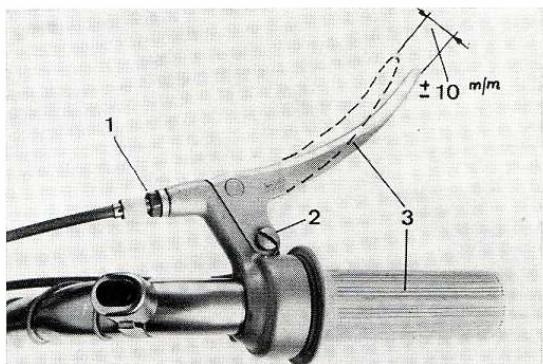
DEMONTAGE DU LEVIER DU FREIN AVANT.
